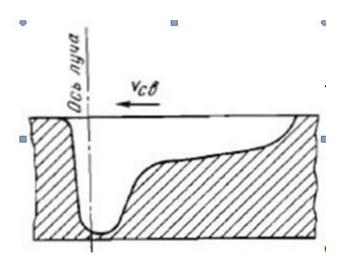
Продольное сечение ванны при лазерной сварке
